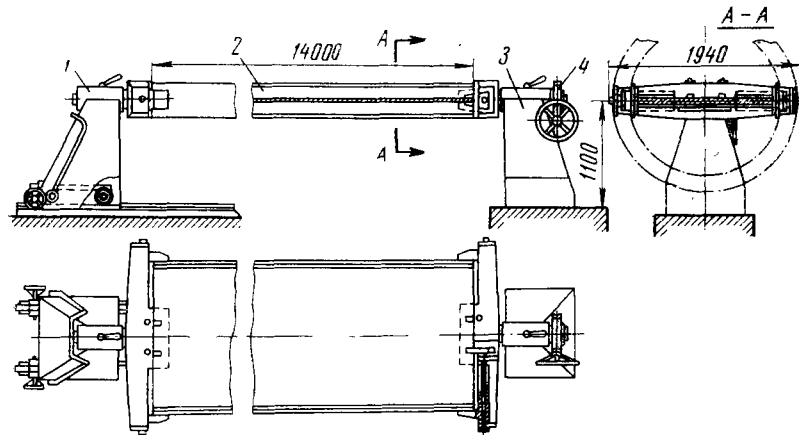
Центральной кантователь для сварки двутавровых балок
